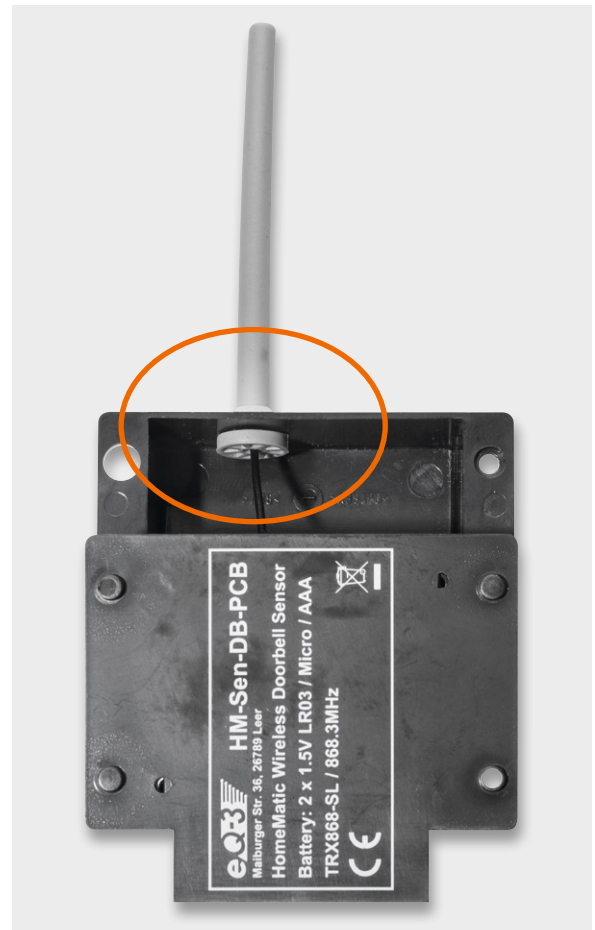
Der Antennendraht wird in die Antennenhülle eingeführt und gleichzeitig das Gehäuseunteil mit der Platine nachgeführt.
